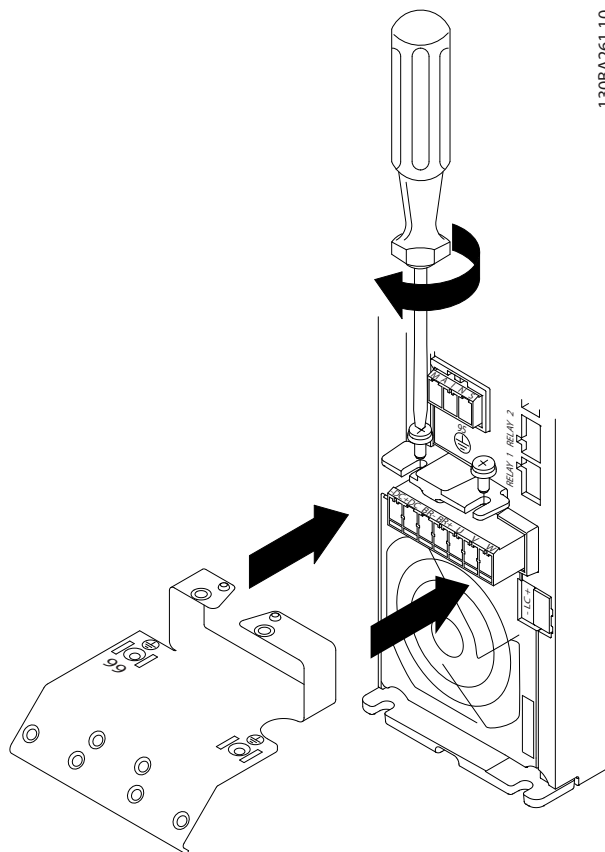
Подключение преобразователя частоты к двигателю, размер корпуса Н9
